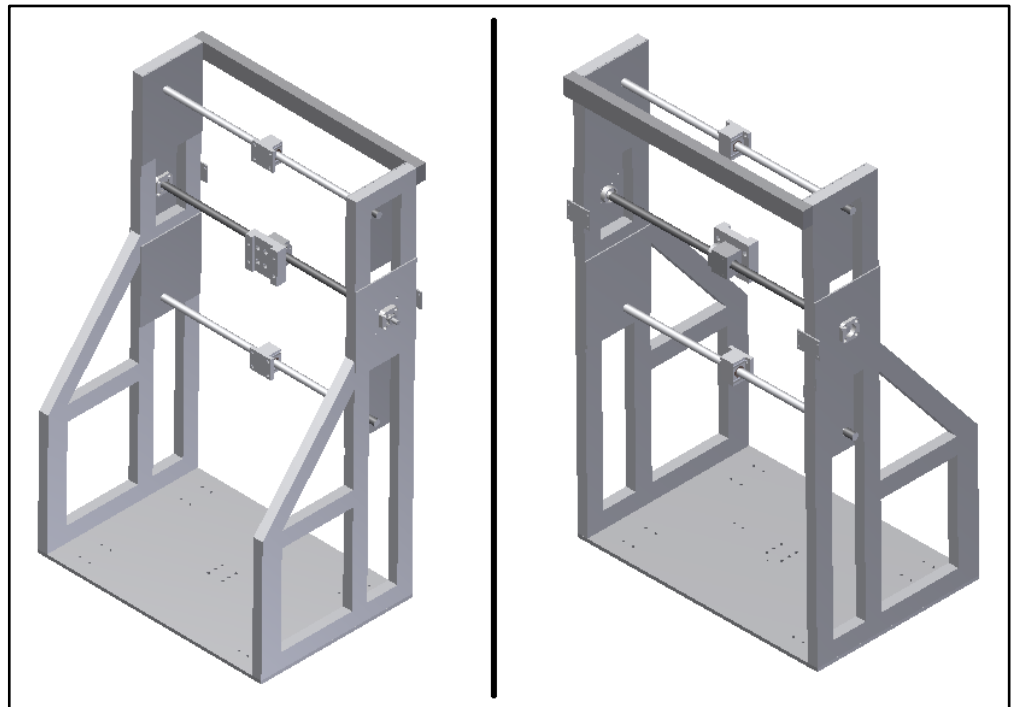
DISPOSICIÓN RODAMIENTOS AXIALES,
